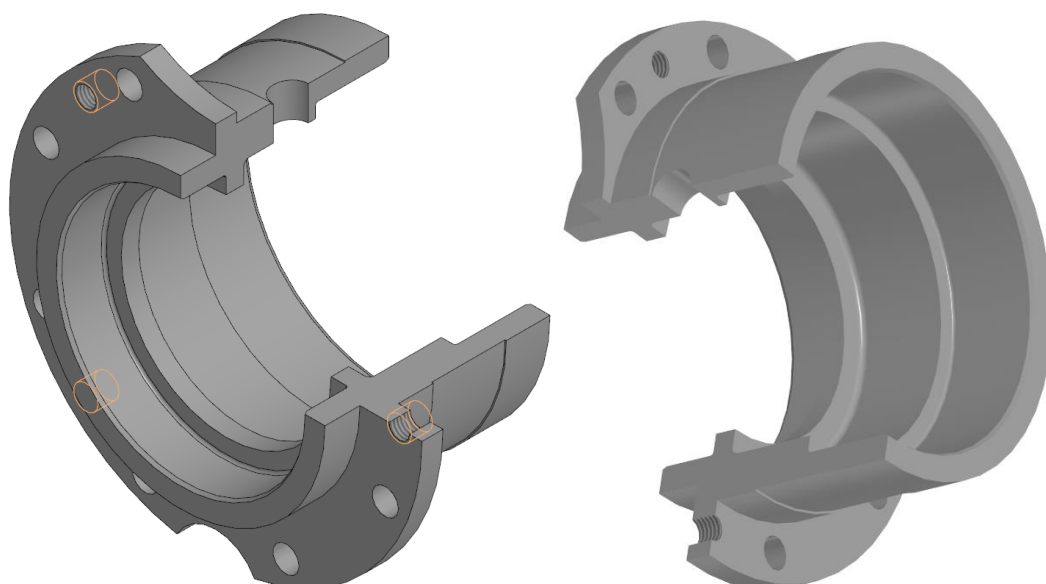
Конфигурация 3D-модели детали «Стакан подшипниковый» с четвертным разрезом
